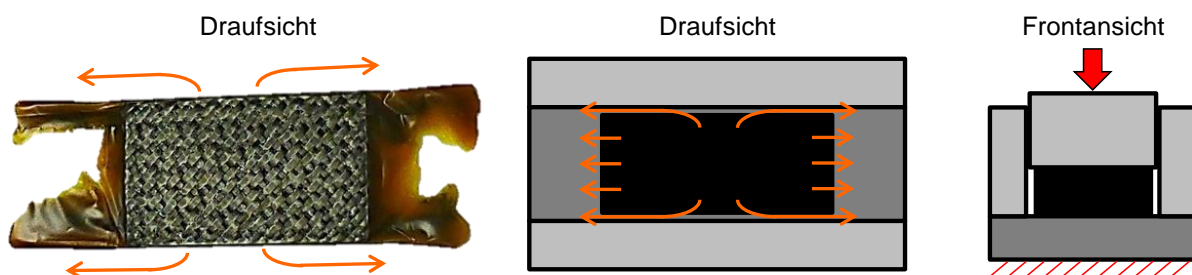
Probe nach dem Verpressen (links); Spalte in der Vorrichtung (Mitte: Draufsicht; rechts: Seitenansicht)
